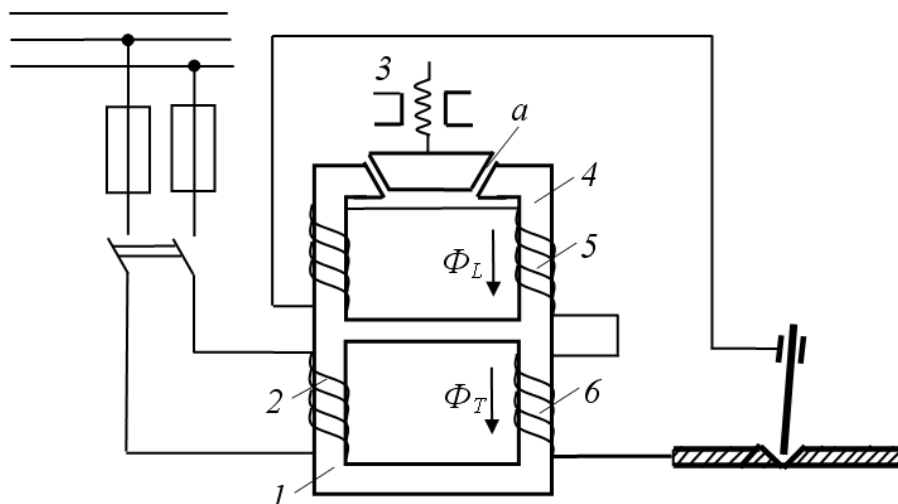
Transformateur de soudage avec une self incorporée :
